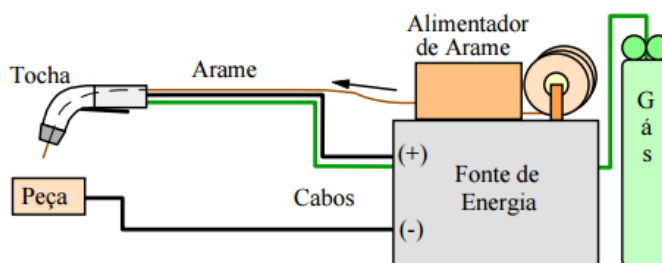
Equipamento básico para soldagem GMAW (Marques 2009)
